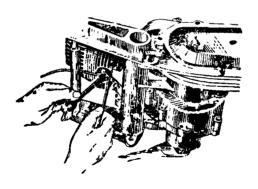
Регулировка натяжения троса управления сцеплением упором на корпусе задней подвески
